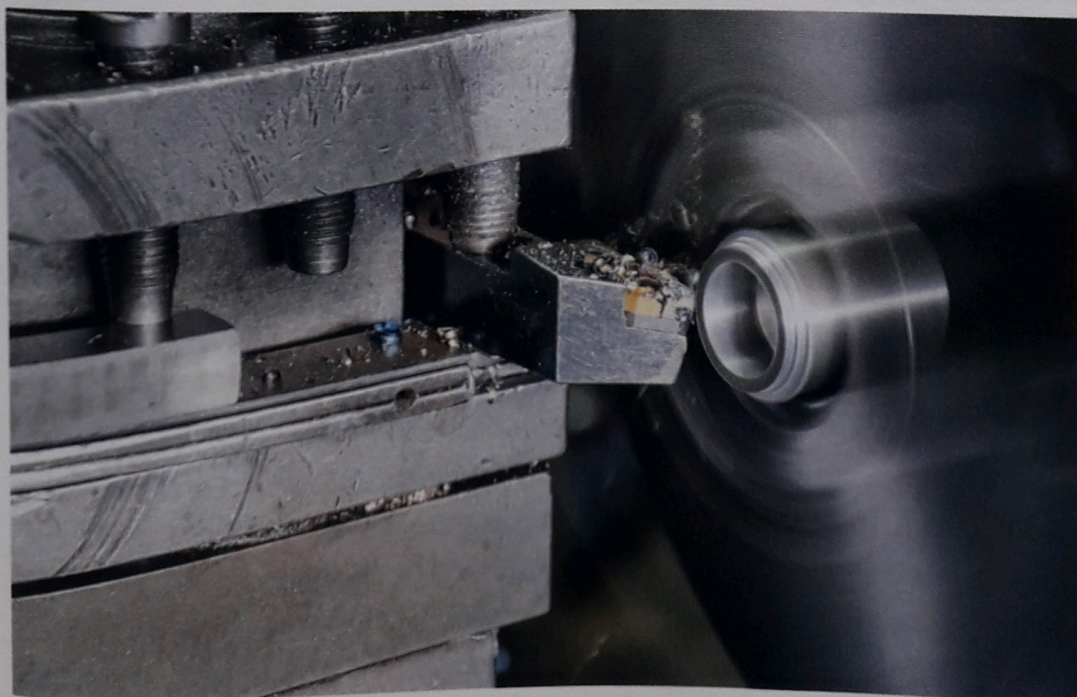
jest wizualizacją ruchu roboczego (obrotowego) obrabianego elementu i ruchu posuwowego (liniowego) narzędzi skrawających.
